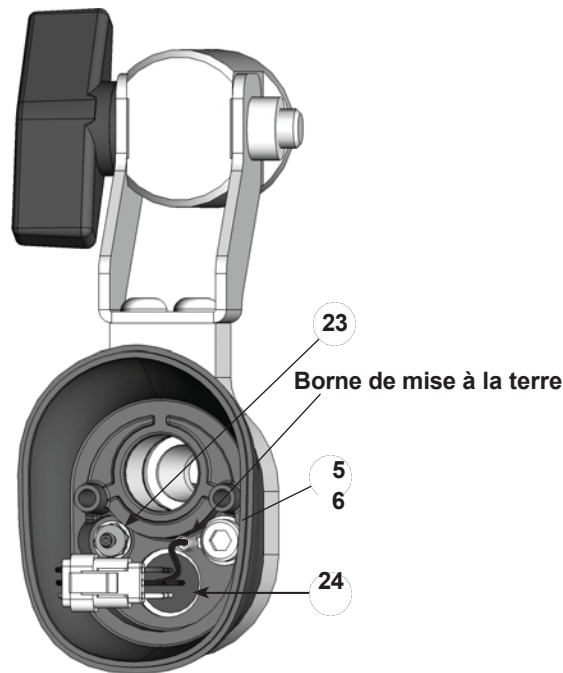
Démontage de l'arrière du pistolet Remplacement du réceptacle de câble et du raccord cannelé de l'arrière
